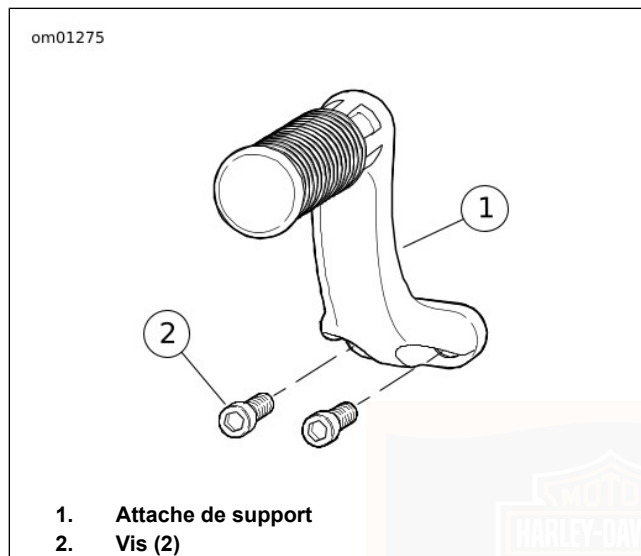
Ensemble de repose-pied gauche de conducteur monté à mi-hauteur : Modèles XL
